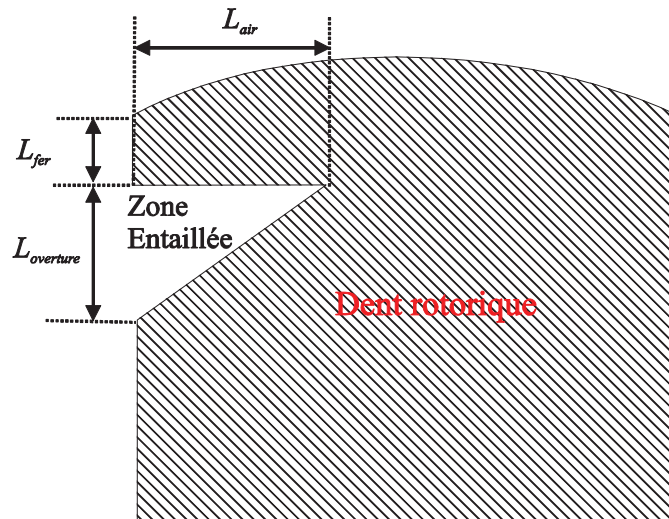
Vue en coupe et dimensions à étudier de la zone entaillée de la MRVNC
